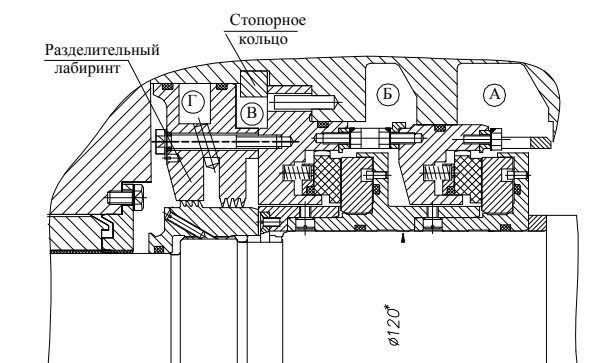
Уплотнение ротора компрессоров агрегатов ГПА-Ц 6,3 (обозначения см. на рис. 2)
